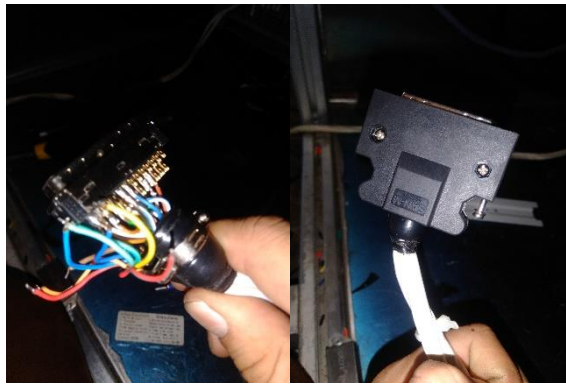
Izquierda: Pines nuevos soldados, derecha: cable terminado
